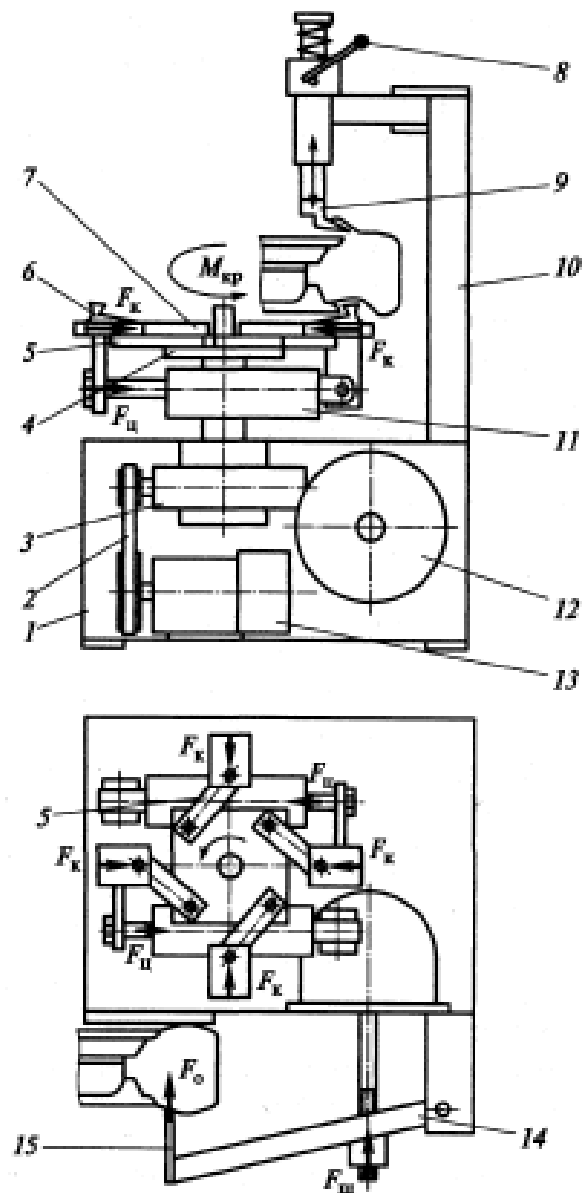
Схема стенда для монтажа и демонтажа шин колес легковых автомобилей (монтажный стол и монтажная стойка на виде сверху не показаны):
